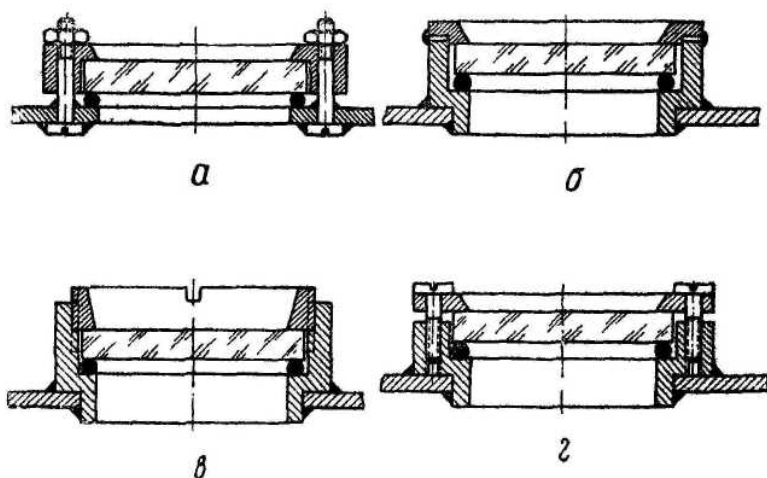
Примеры конструктивного крепления иллюминаторов: а — на винтах; б — паяное; в — на резьбе; г — с помощью прижимной (на винтах) шайбы
